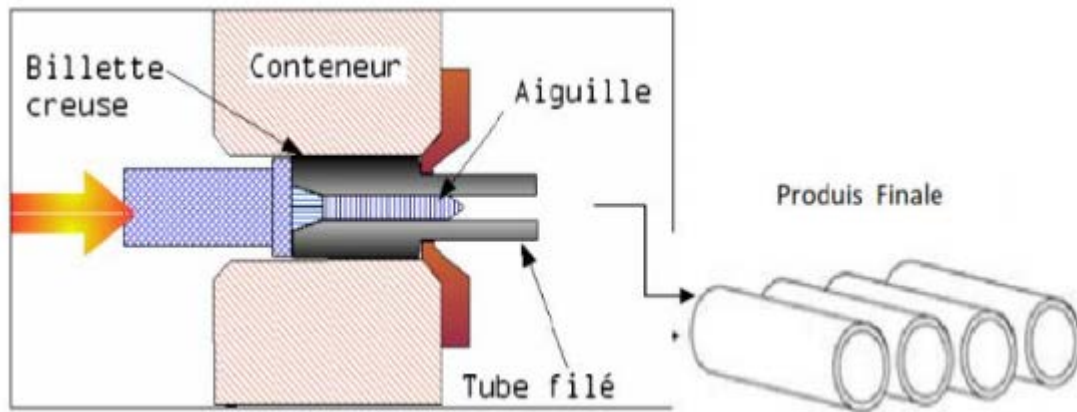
Fabrication de pipeline sans soudure
